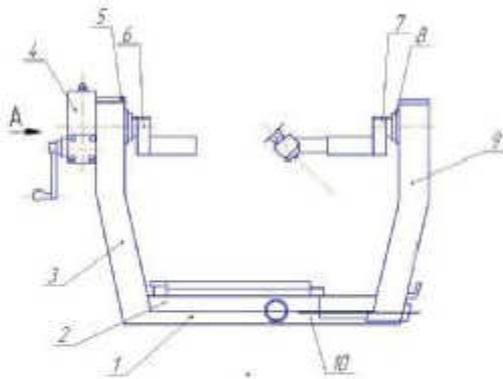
Стенд для разборки и сборки двигателей (модель С 152)
